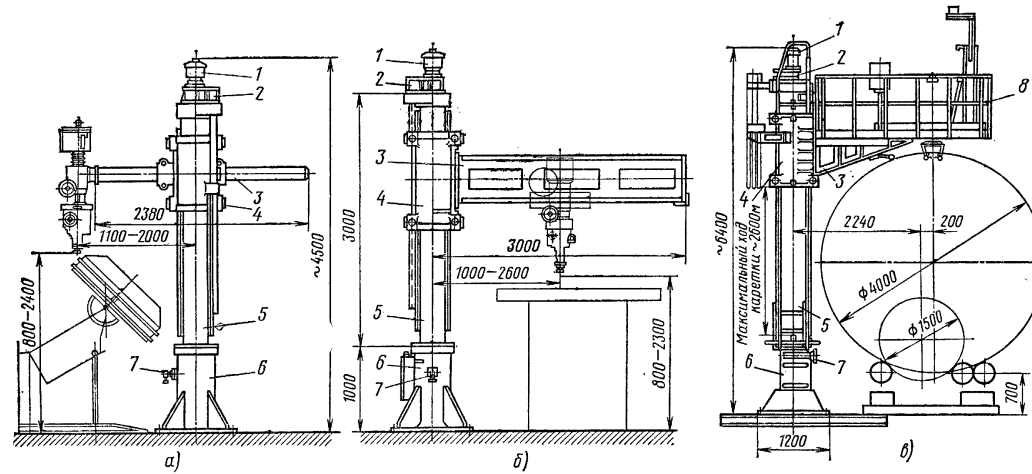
Колонны поворотные для сварочных автоматов:
